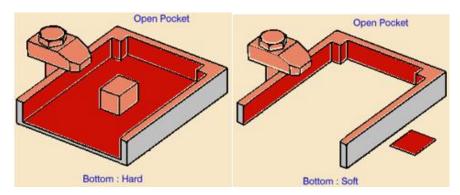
Open Pocket: Bottom Hard/ Soft.
